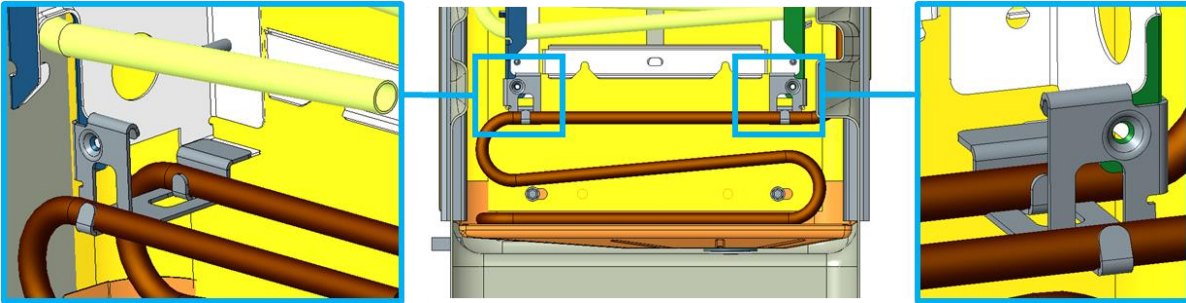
Imagen del montaje de la propuesta 1 en CAD
